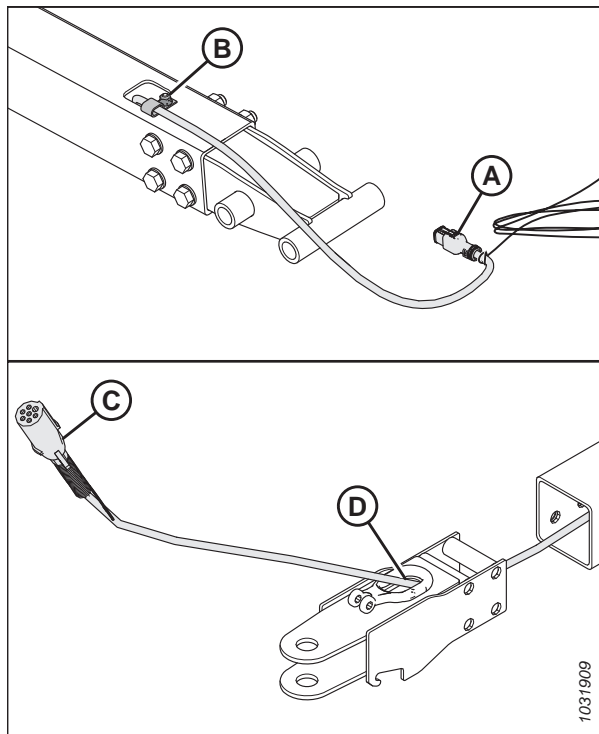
Extracción del adaptador de remolque de la horquilla
